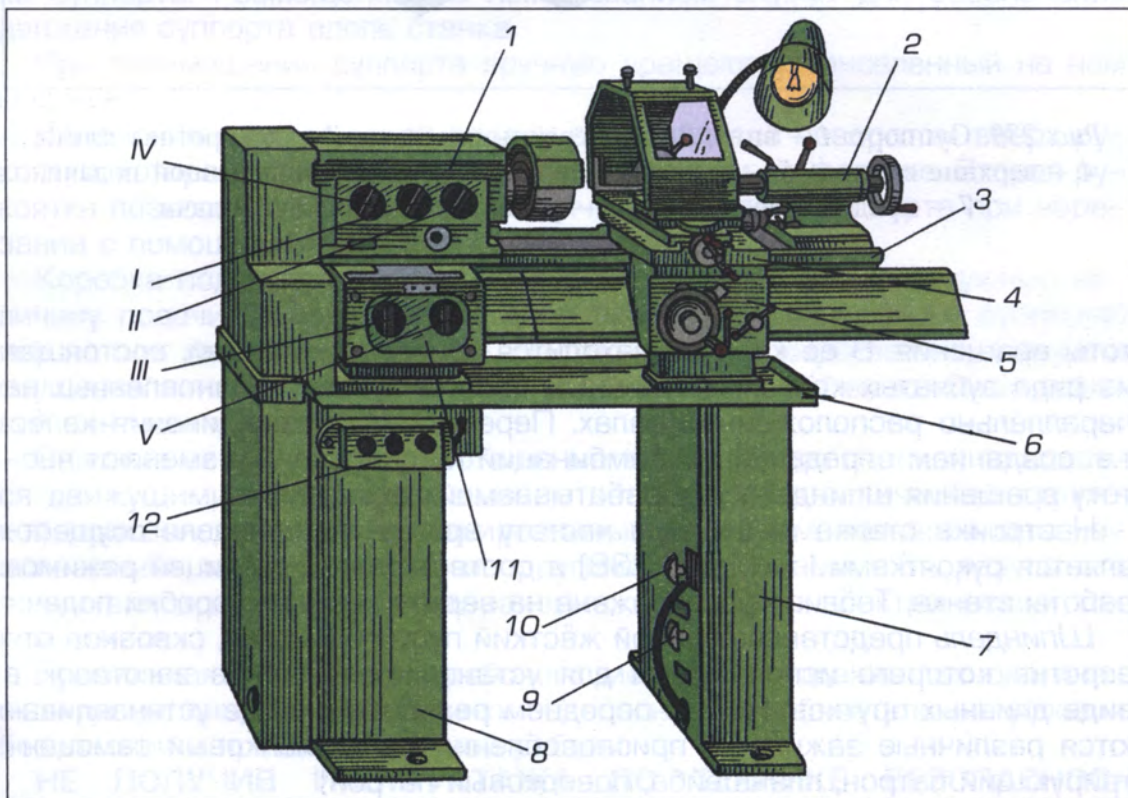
Устройство токарно-винторезного станка ТВ-6: I и II – рукоятки настройки частоты вращения шпинделя (n об/мин), III – рукоятка настройки величины подачи (s мм/об), IV – рукоятка реверса подачи (л-н-п), V – рукоятка включения ходового вала или ходового винта, 1 – передняя бабка, 2 – задняя бабка, 3 – станина с продольными направляющими, 4 – суппорт, 5 – фартук суппорта, 6 – поддон, 7 – задняя тумба, 8 – передняя тумба, 9 – пакетный выключатель сети (общий), 10 – пакетный выключатель местного освещения, 11 – коробка подач, 12 – пусковая коробка
